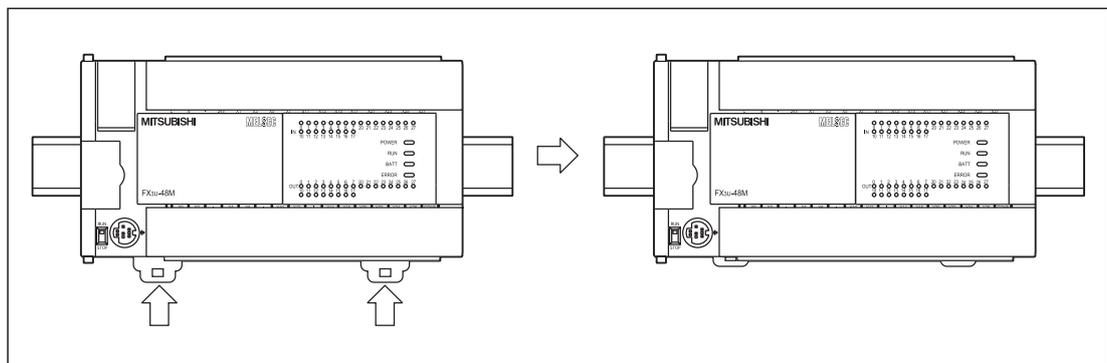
Ante del montaje en un carril DIN hay que tirar de las bridas de montaje hacia abajo.
